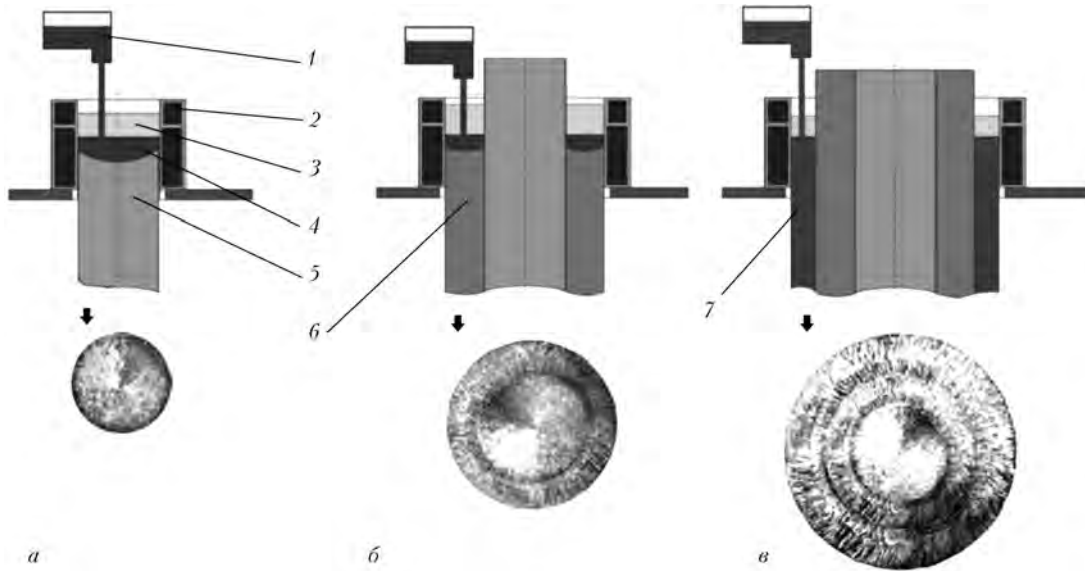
Схема укрупнения слитков последовательным кольцевым ЭШНУ ЖМ: *а* – выплавка исходного слитка; *б* – однократное электрошлаковое наплавление; *в* – последовательное двукратное наплавление; 1 – заливочное устройство для подачи жидкого металла в кристаллизатор; 2 – токоподводящий кристаллизатор; 3 – шлаковая ванна; 4 – металлическая ванна; 5 – центральный слиток; 6, 7 – слой металла соответственно после одно- и двукратного наплавления
